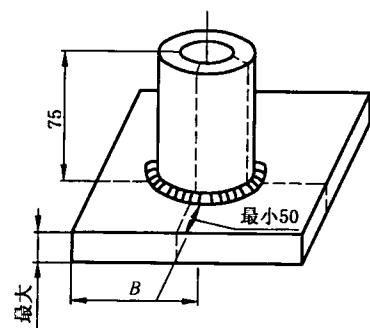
管板角焊缝试件及宏观金相试样
